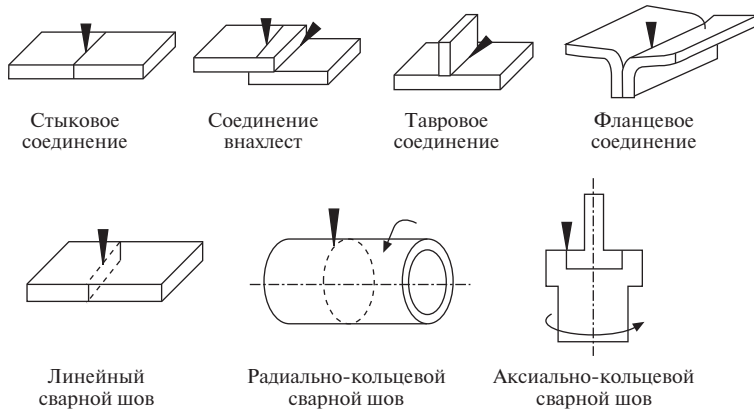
Примеры типовых видов сварных соединений, получаемых с помощью лазерной сварки
